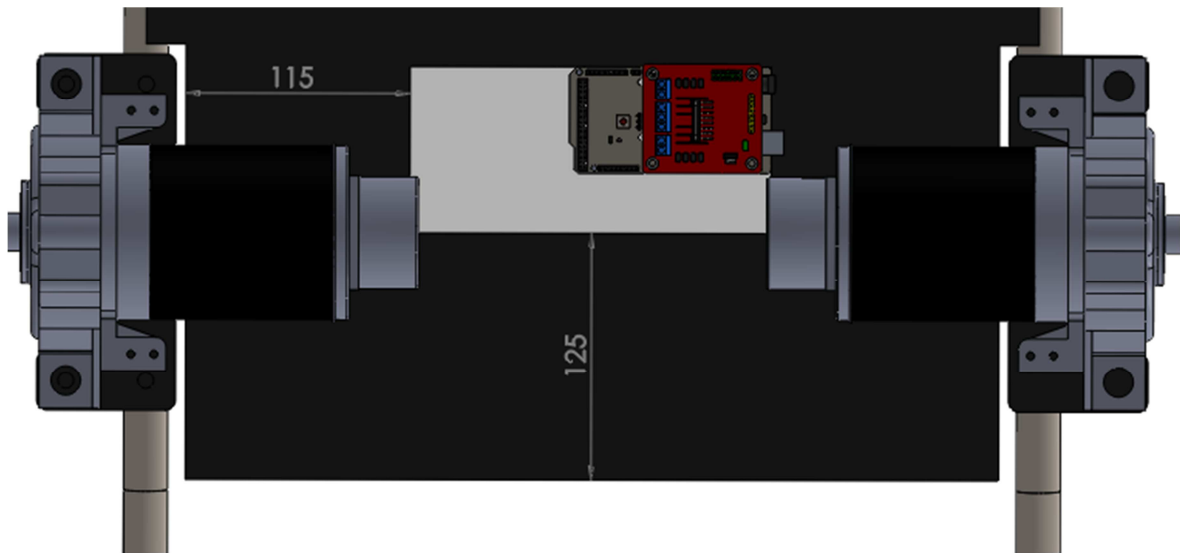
Ubicación de la placa electrónica para conexión de componentes sobre la plancha de soporte para la batería.
